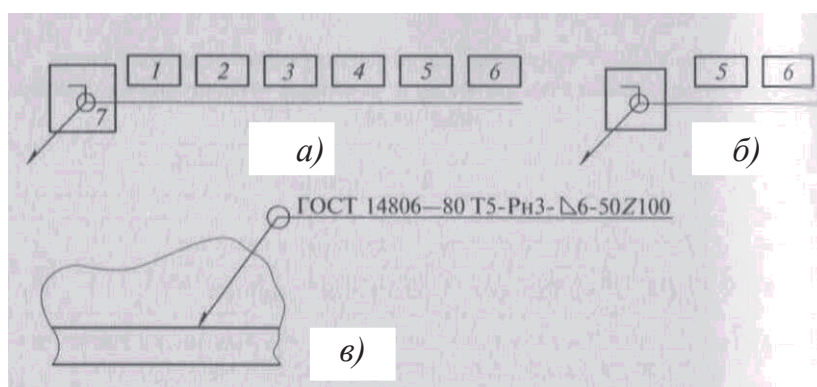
Форматы записи при обозначении сварных швов: а – стандартного; б – нестандартного; в – пример обозначения
